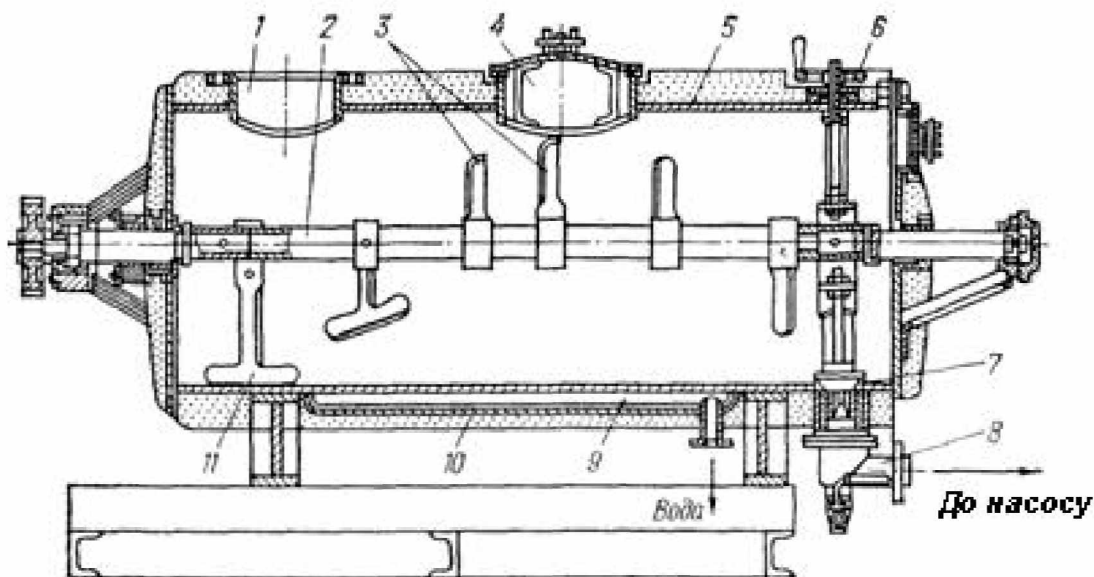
Горизонтальний лопатевий змішувач ШС: 1 – завантажувальний люк; 2 – горизонтальний вал; 3 – плоскі лопаті; 4 – оглядовий люк; 5 – циліндрична камера; 6 – гвинтовий привод клапана; 7 – конічний випускний клапан; 8 – зливальний патрубок; 9 – водяна сорочка; 10 – теплоізоляція; 11 – Т-подібна лопать.
